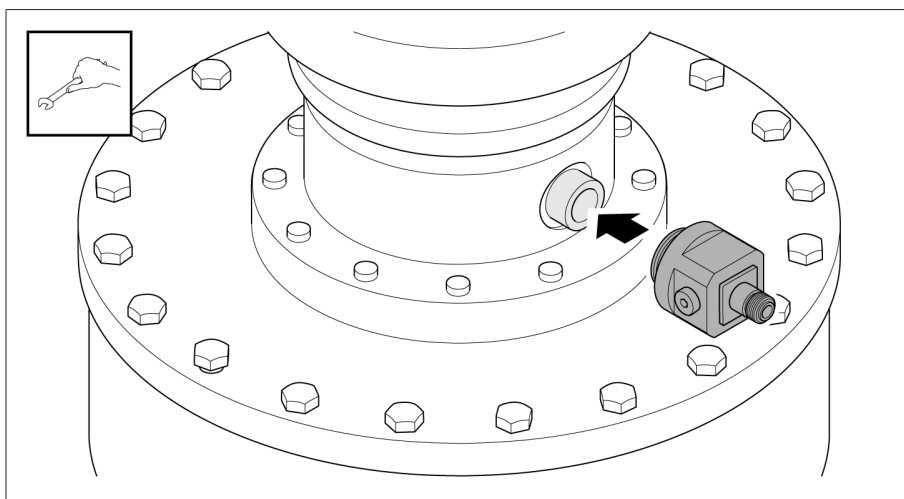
Montaje del adaptador para aislador pasante (ejemplo con el adaptador para aislador pasante A002)
